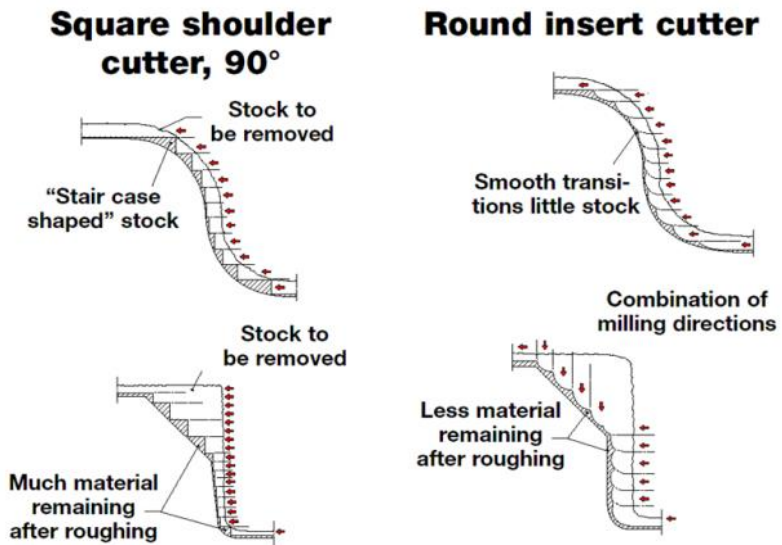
Coromant in Die and Mould Making(sandvik)
